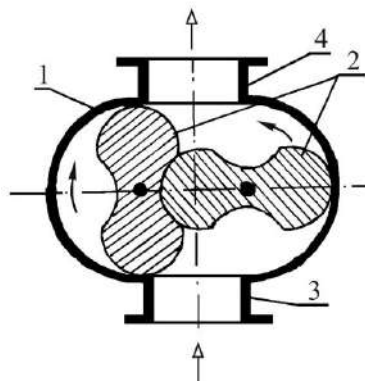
Компрессор с двумя вращающимися поршнями:
